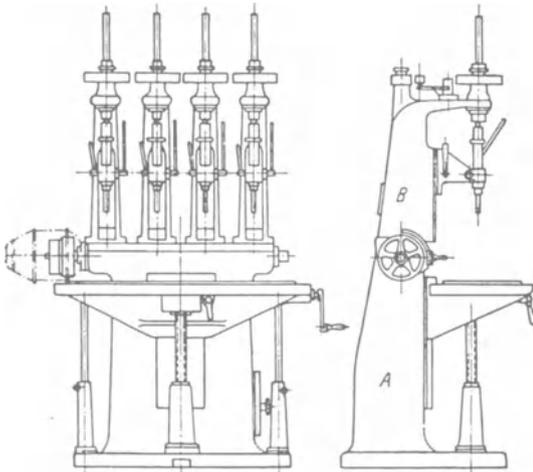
u. 261. Mehrspindelbohrmaschine.
